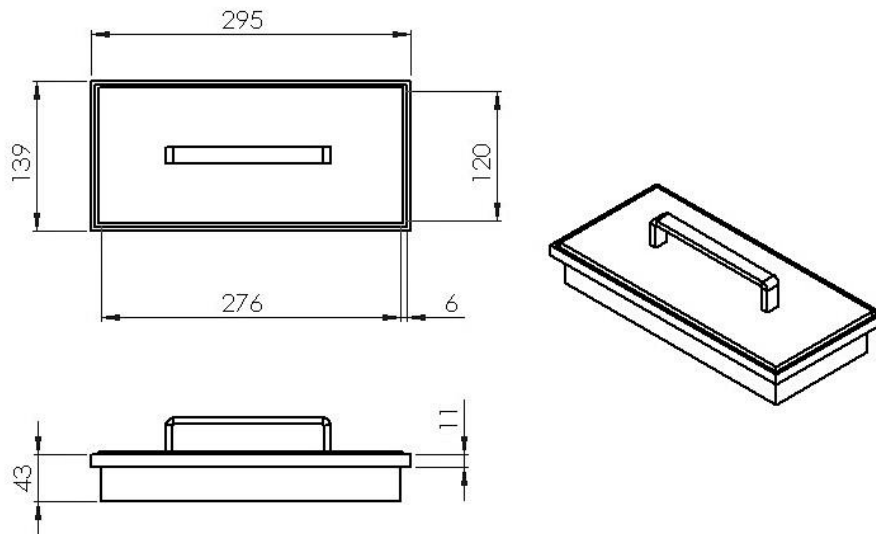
Dimensiones externas de la caja y su tapadera. Cotas en mm.
